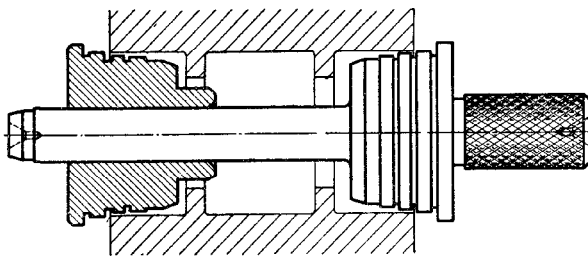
Конструкция ступенчатой цилиндрической оправки
